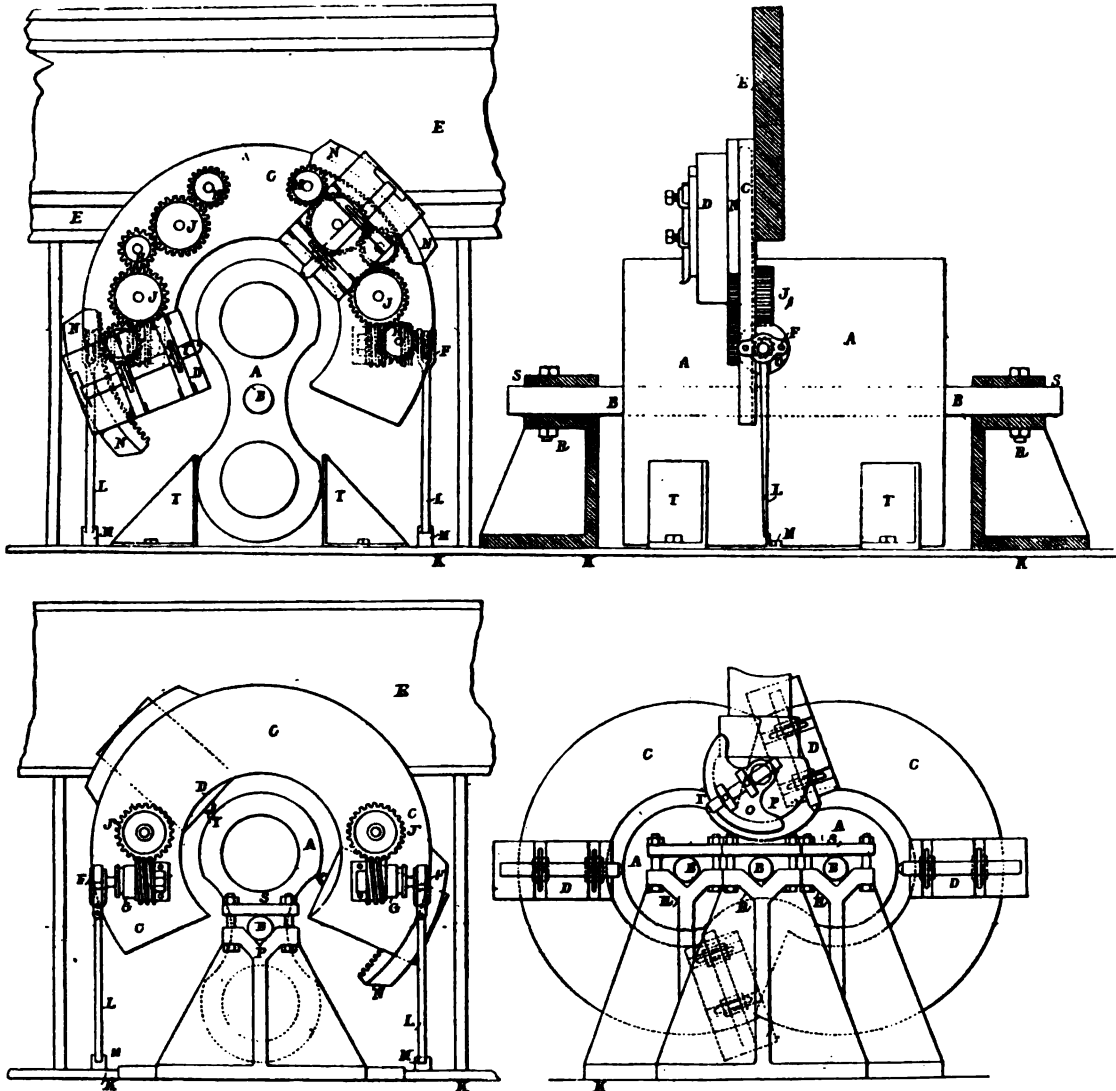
à 471. — Machines *Thwaites* pour la fabrication des pistons de pompes (fig. 472 et 473) entièrement en fer.
